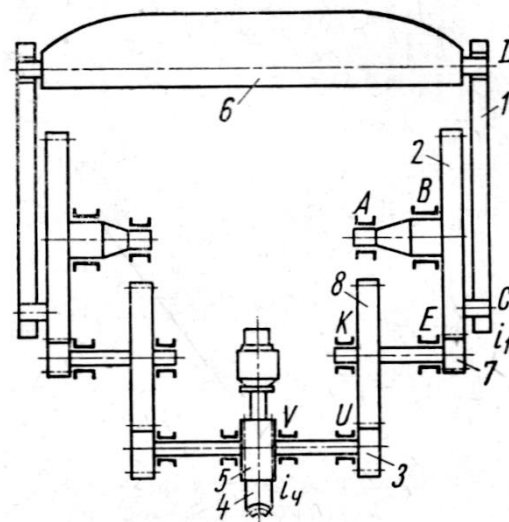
Схема приводу форматора-вулканізатора 55"
